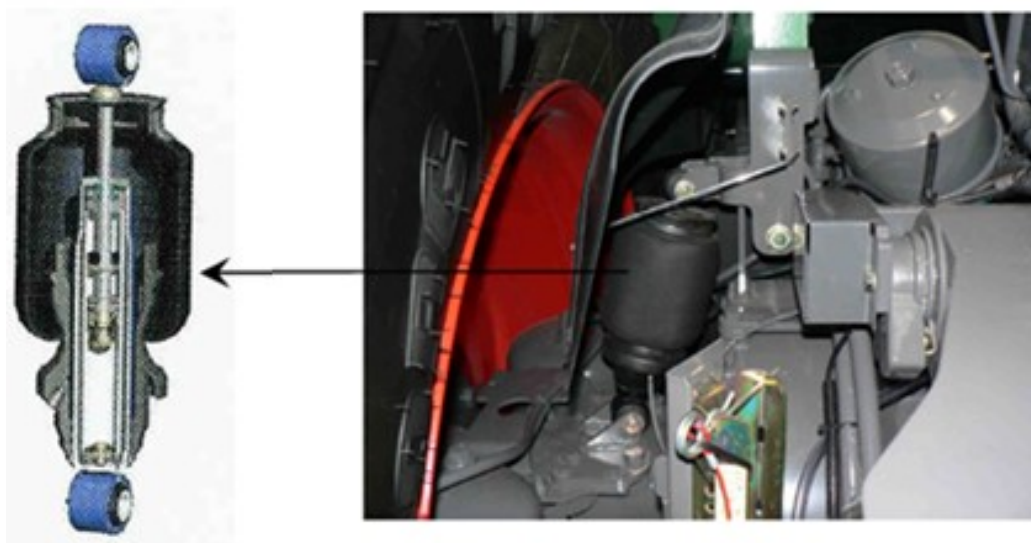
Celkové provedení uložení kabiny pomocí mechanického odpružení [5]
